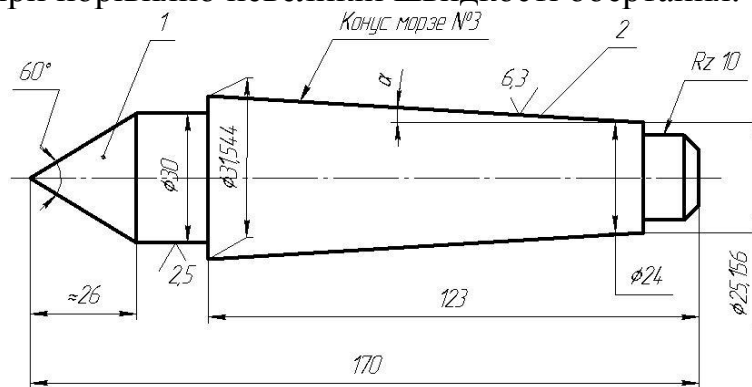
Жорсткий опорний центр: 1 – робочий конус, 2 – хвостовик
